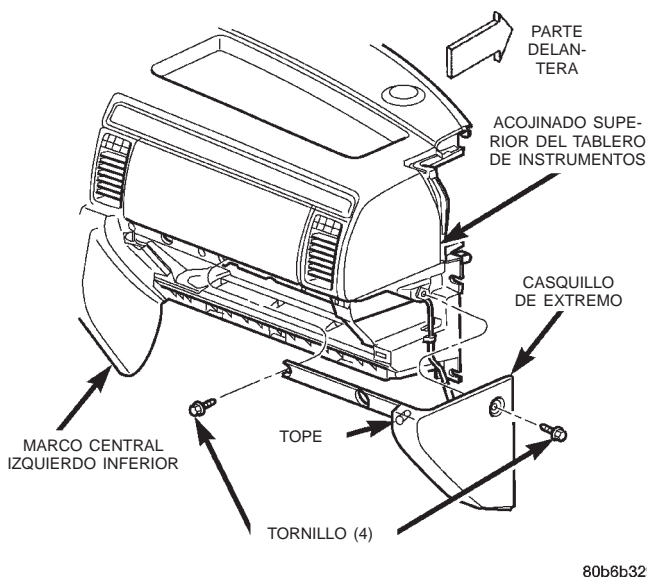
Desmontaje e instalación del casquillo de extremo del tablero de instrumentos
